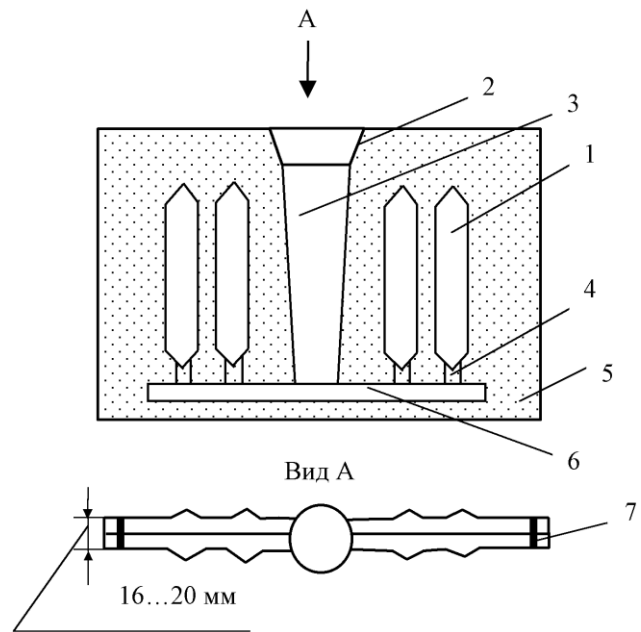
Схема подвода металла к отливкам радиаторов в оболочковые формы: 1 — отливка радиатора; 2 — литниковая чаша; 3 — стояк; 4 — питатели; 5 — форма; 6 — шлакоуловитель; 7 — скоба для фиксации половинок оболочек
